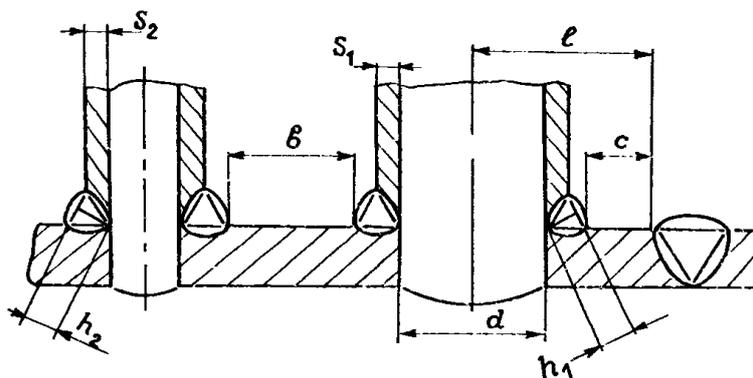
Расположение сварных соединений приварки патрубков:
